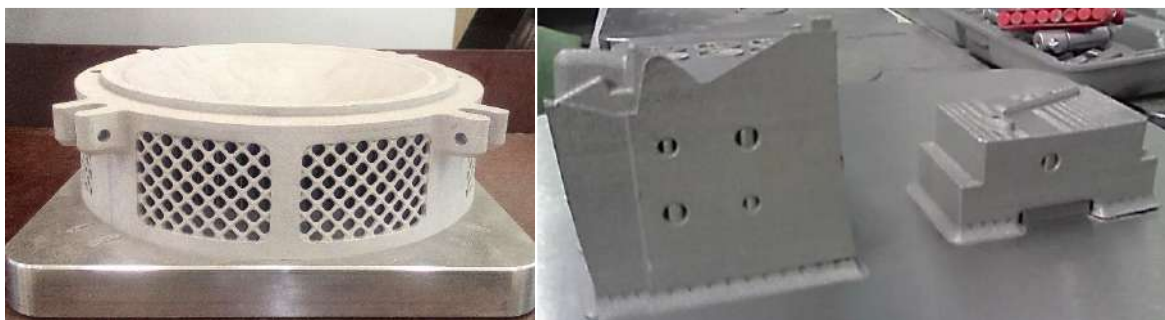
Детали пресс-формы, изготовленные методом селективного лазерного сплавления
